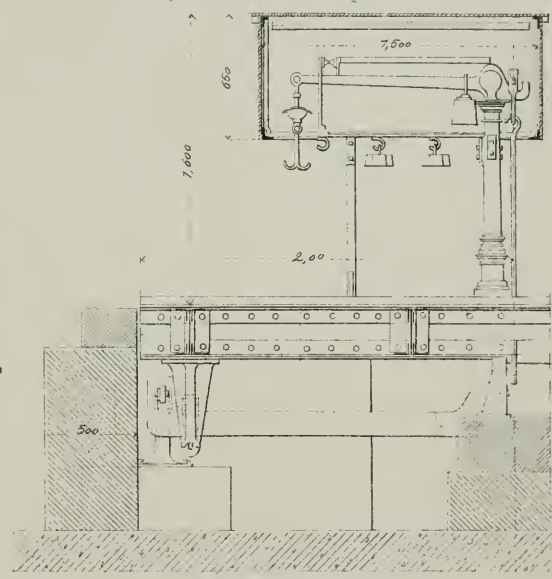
Elevation du tablier & des leviers à 0,025 pour 1^m
